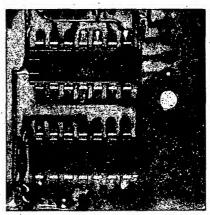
Tvar spojů a rozložení součástí generátoru z obr. 96
